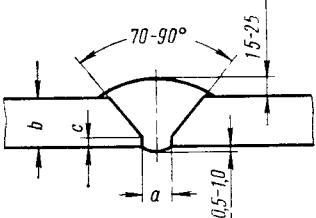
Схема сварки с устранением горячеломкости
